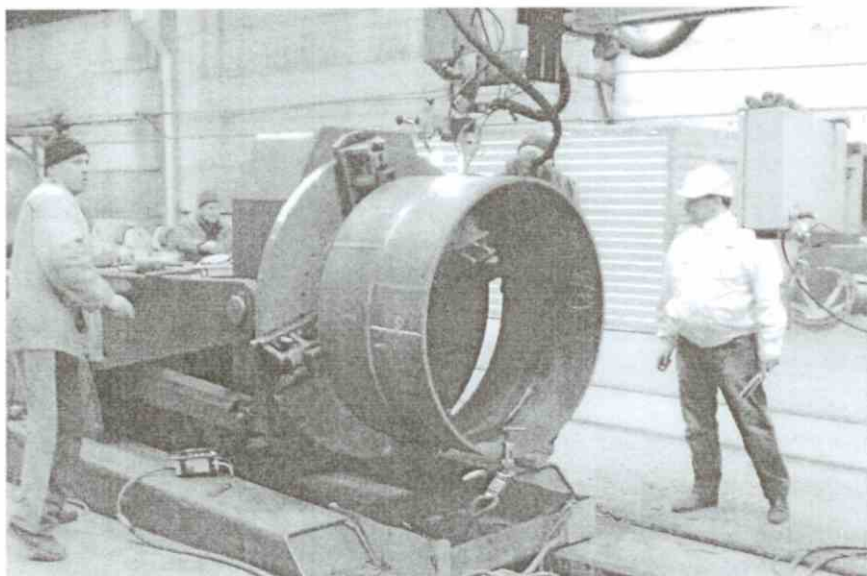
Сварка поворотного кольцевого стыкового соединения катушек
